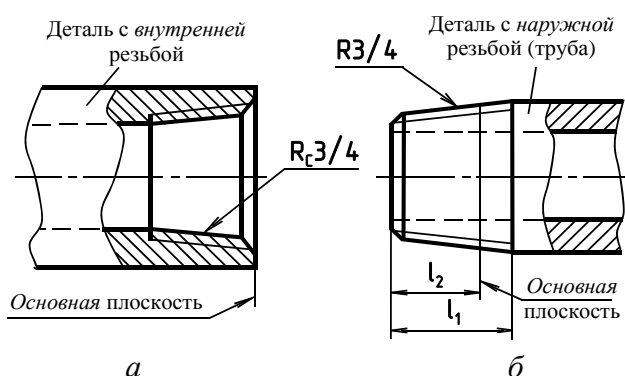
Обозначение на чертеже трубной конической резьбы: а – внутренней; б – наружной
